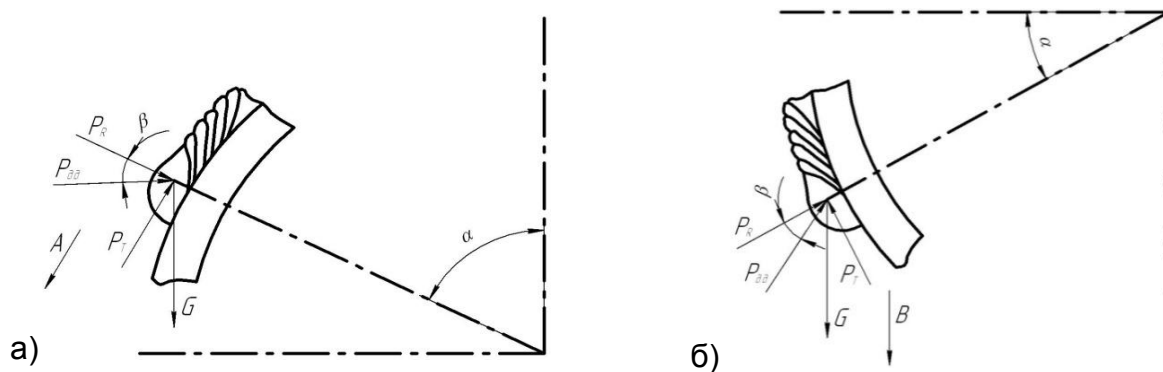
Схема сил, действующих на сварочную ванну:
